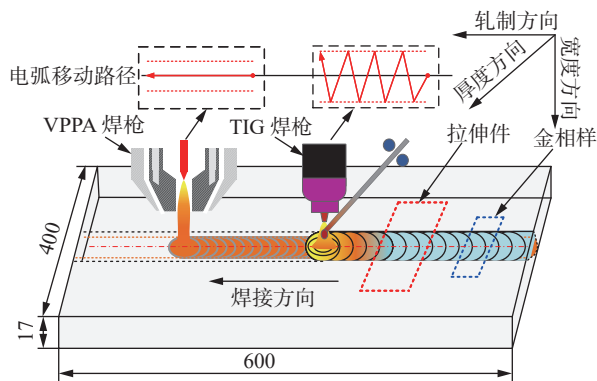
VPPA-TIG 复合焊示意图 (mm)
